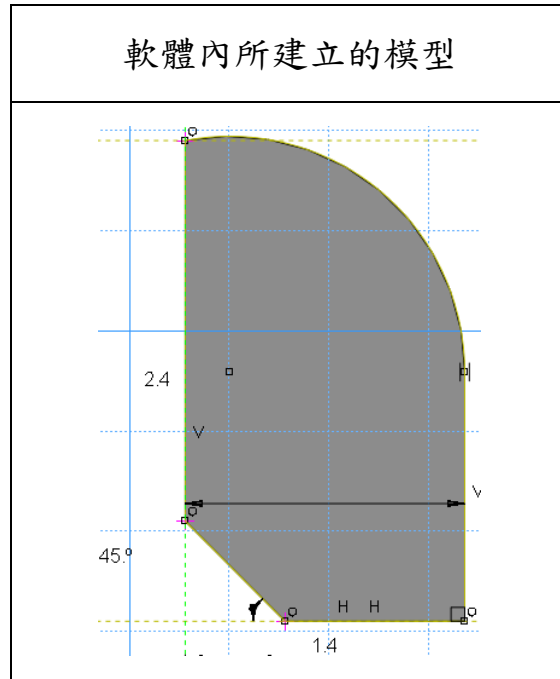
橡膠 o-ring 墊圈尺寸圖(單位：mm)
